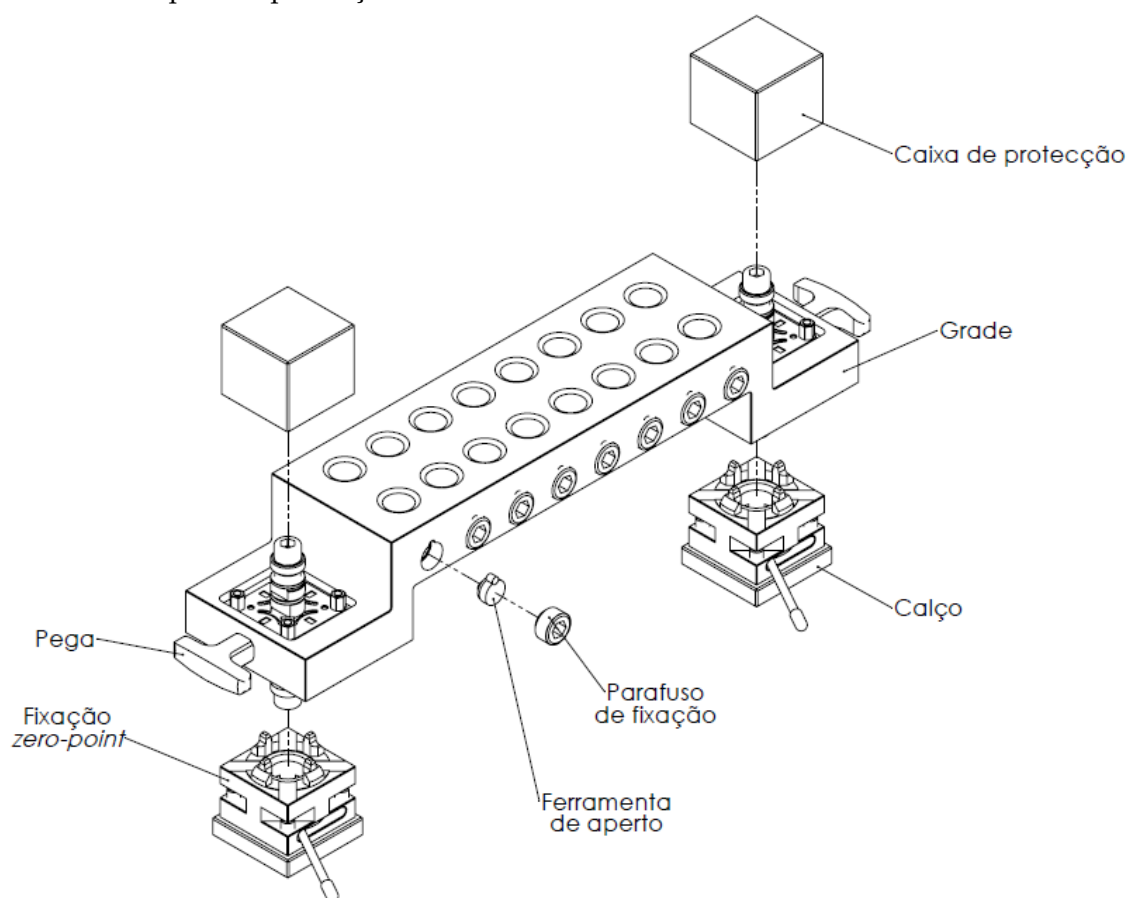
Perspectiva explodida do sistema de fixação projectado
